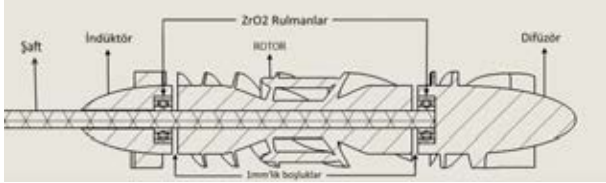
Lazer Sinterlemeyle Üretilmiş Pompa Parçaları
